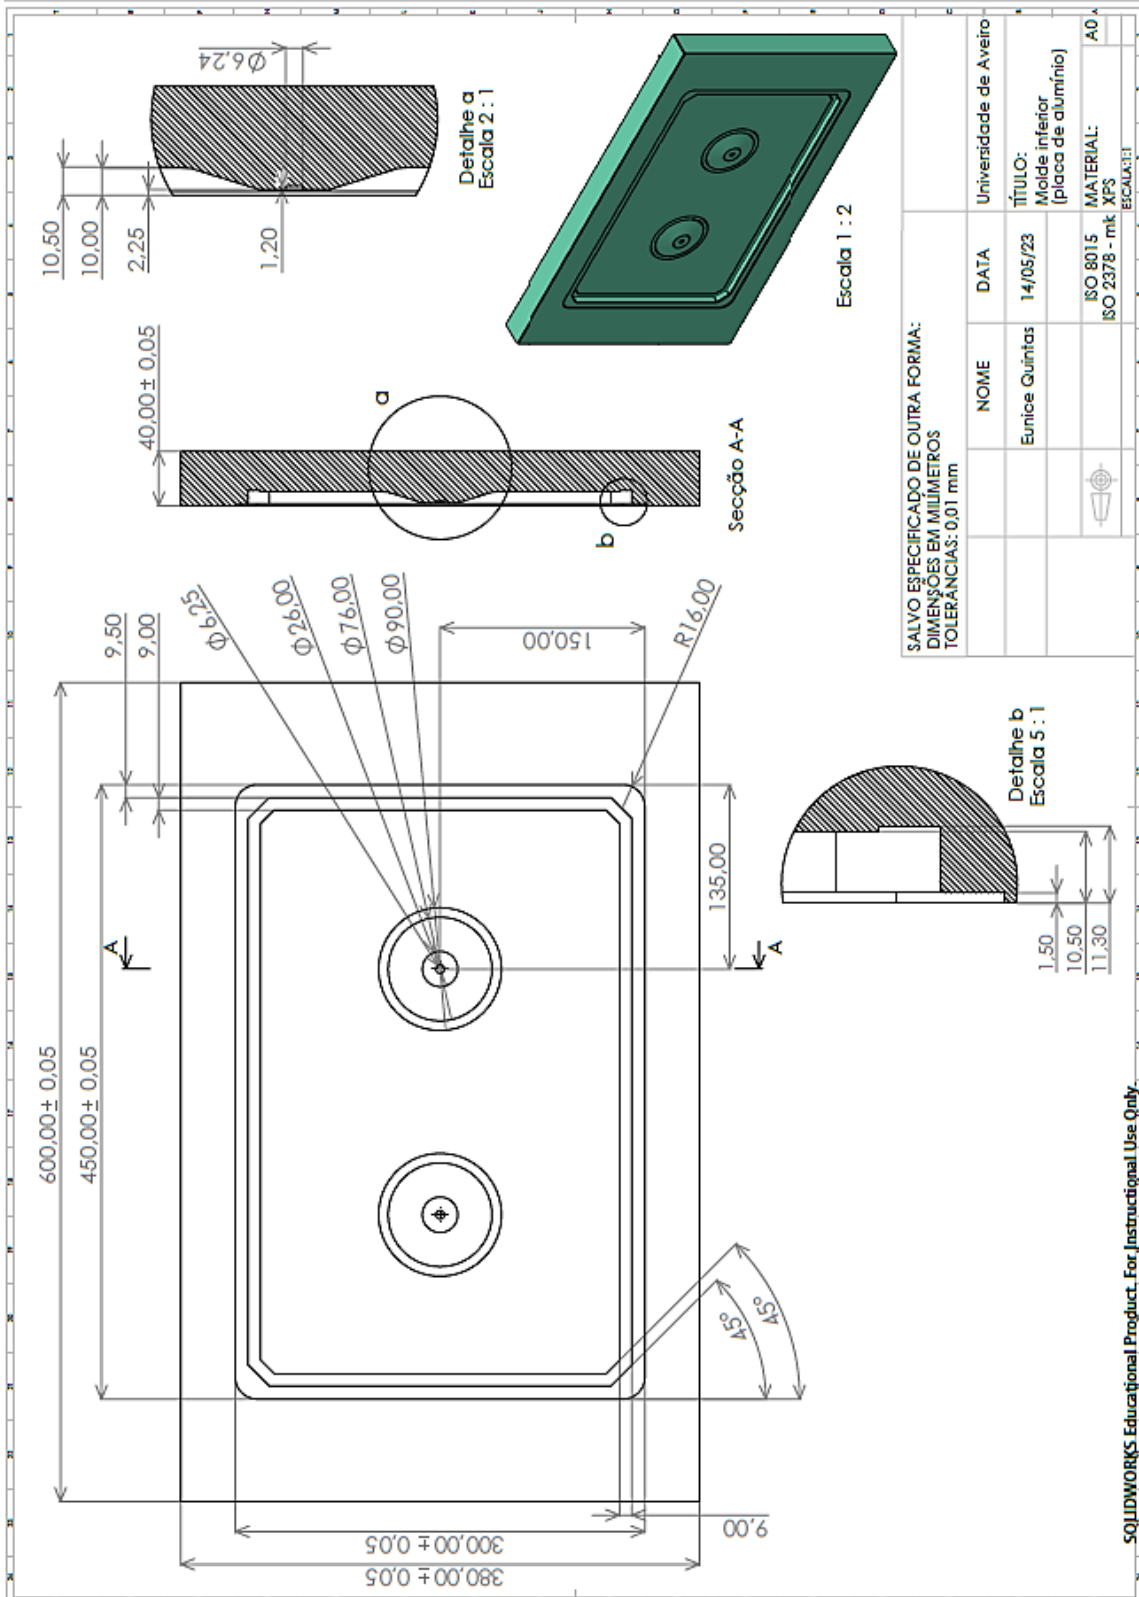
Desenho técnico do molde inferior de XPS para a placa de alumínio.
